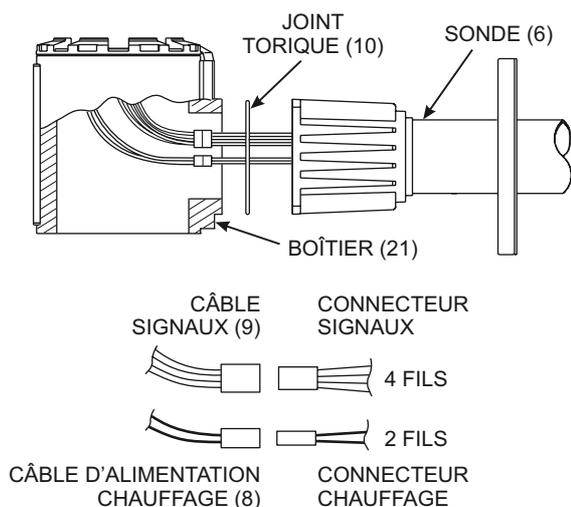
Sonde pour électronique séparée : câblage tube de sonde – boîtier
